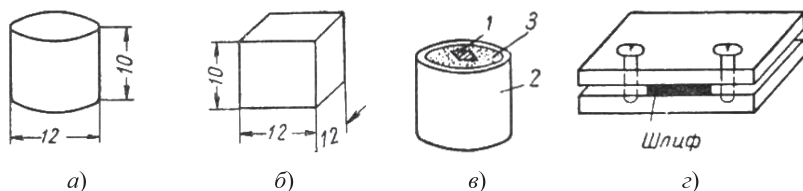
Нормальные размеры металлографических образцов (а, б) и приспособления для закрепления образцов (в, г): 1 – образец; 2 – металлическая трубка; 3 – легкоплавкий сплав или эпоксидная смола
